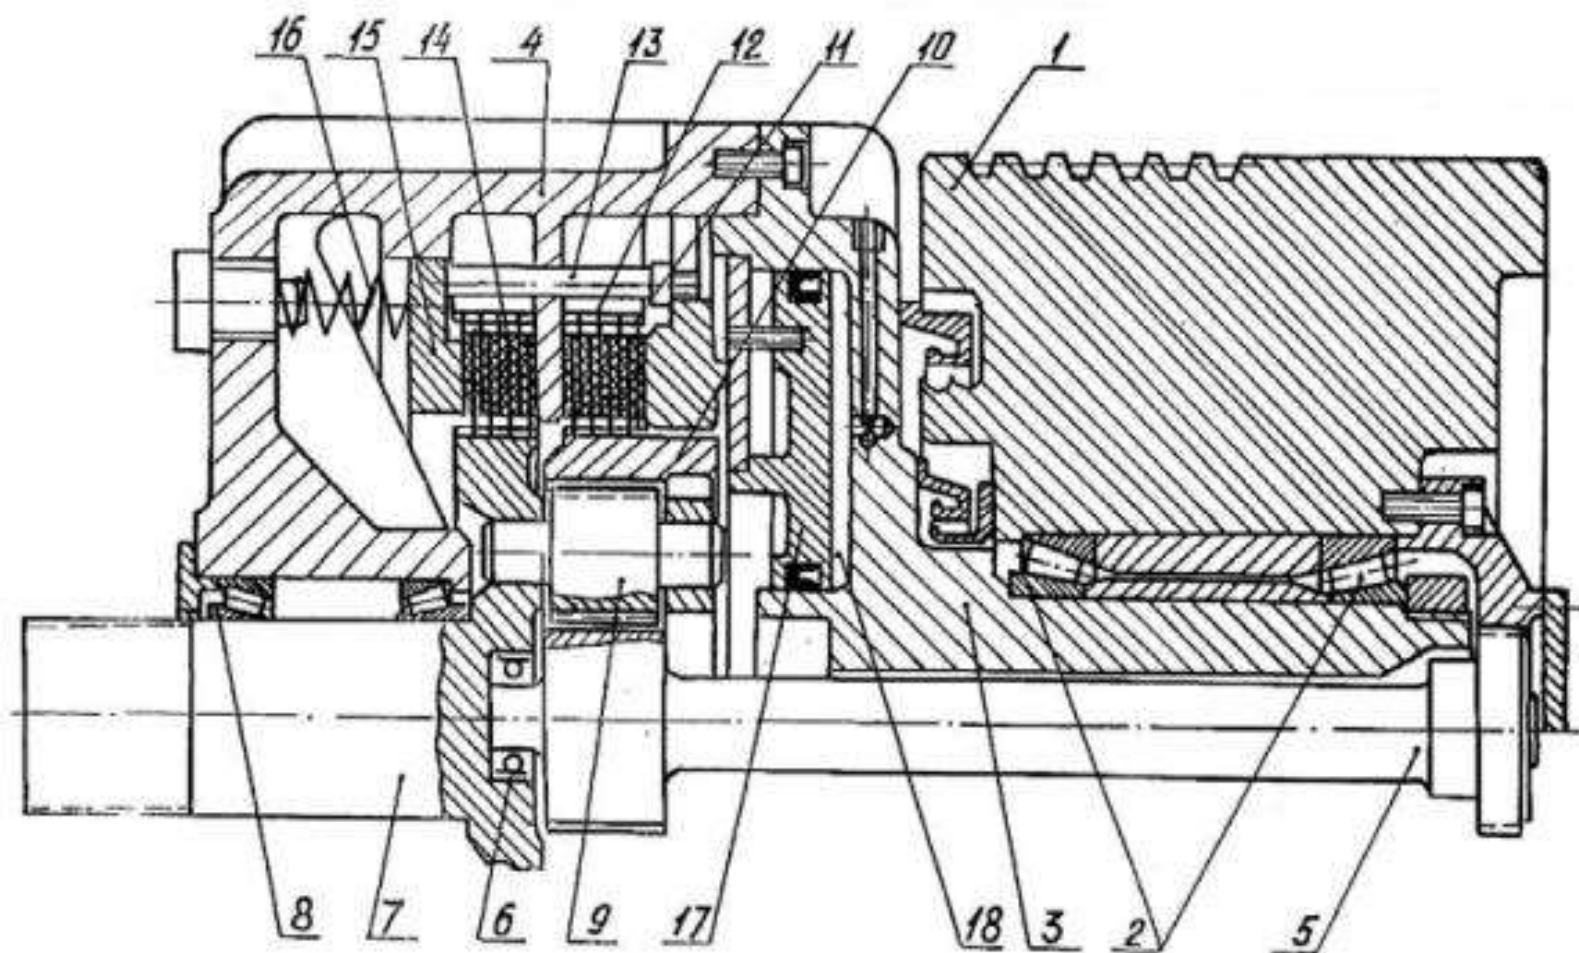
Планетарный привод «TORC-PAC»
